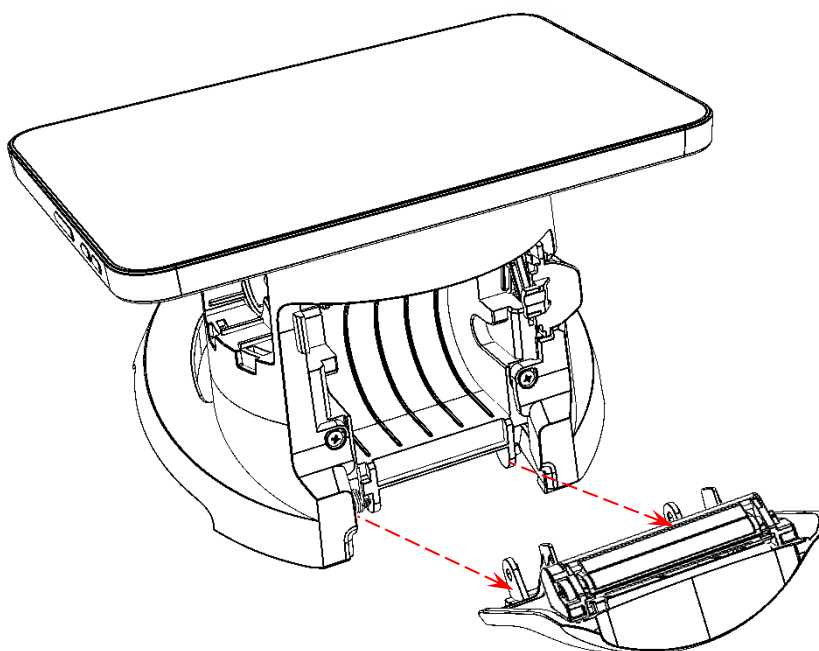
Отделение крышки лотка для ЧД от корпуса
